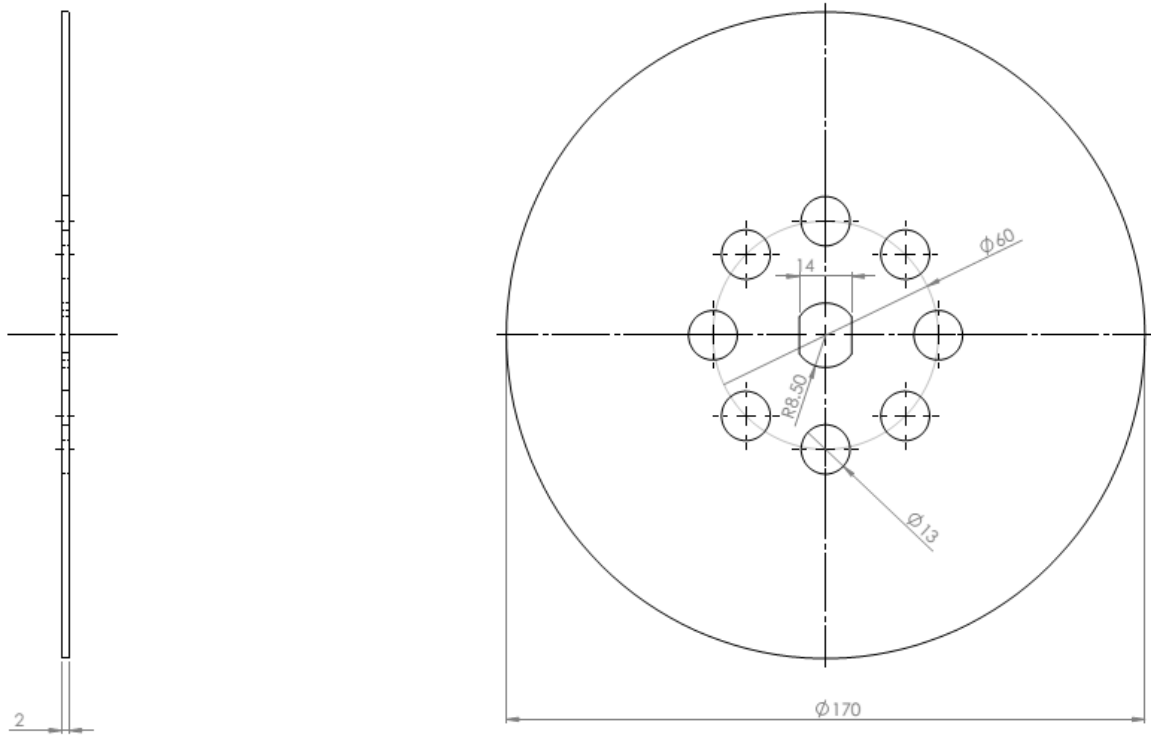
Dimensões (em milímetros) dos discos do rotor tipo K.
